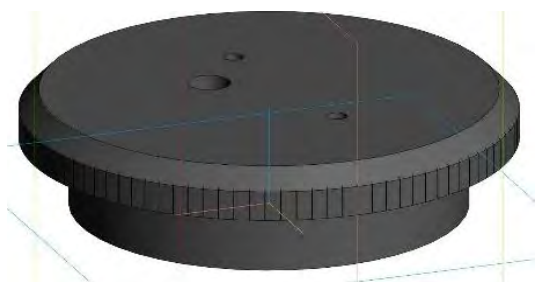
3D модель корпуса прессовой оснастки для прессования столбика во времязадающее кольцо ПИМа.
